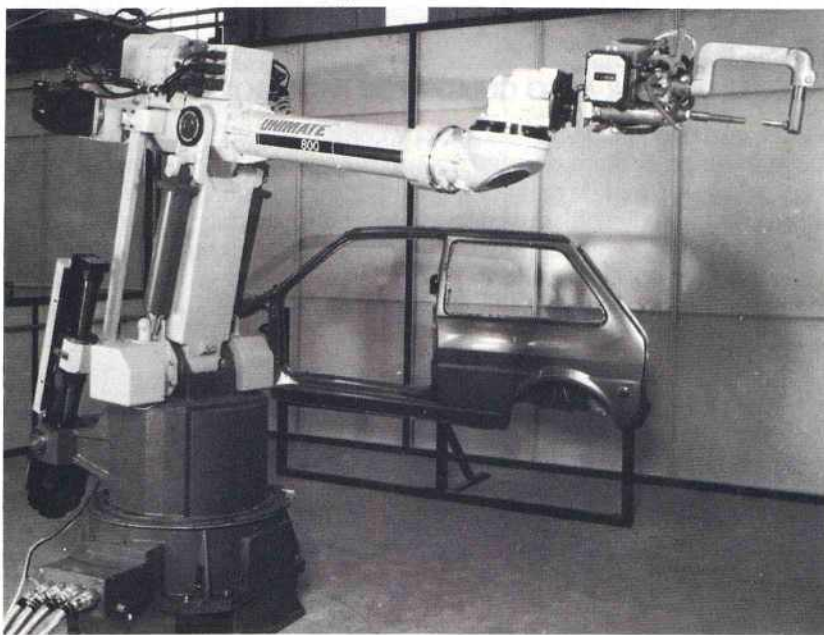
Movimiento de un robot utilizado para la soldadura de chapas de coche.
